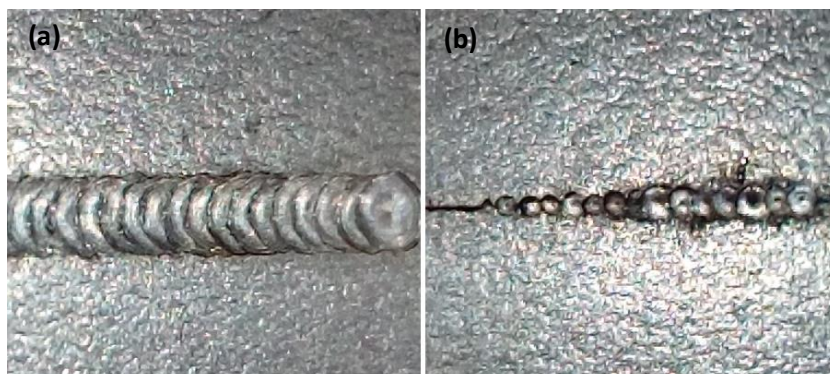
Soldadura laser (partes superior (a) e inferior (b)) com a caixa
